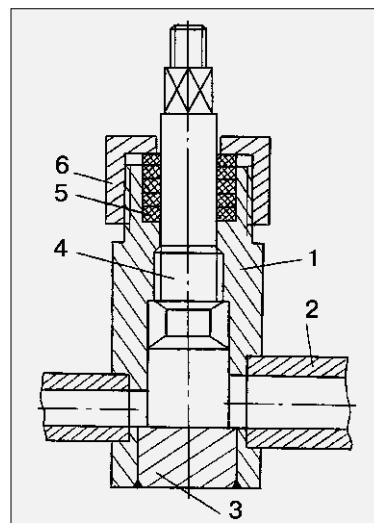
Вентиль с расходной шайбой CO₂: 1 – корпус; 2 – трубы подачи углекислого газа после регулятора давления; 3 – заглушка; 4 – дозирующий винт-шток; 5 – уплотнители; 6 – обжимная гайка
